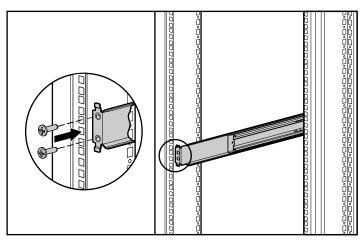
Collegamento della staffa di montaggio alla parte anteriore del rack
